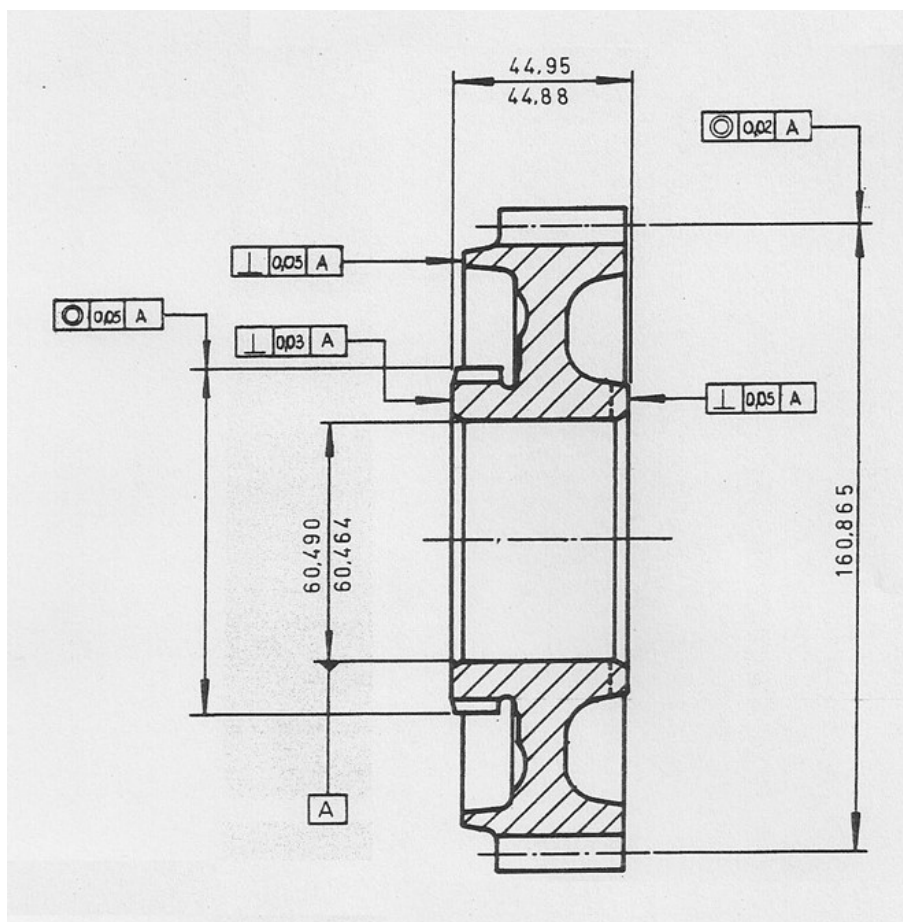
Indicações de tolerâncias em engrenagem.
